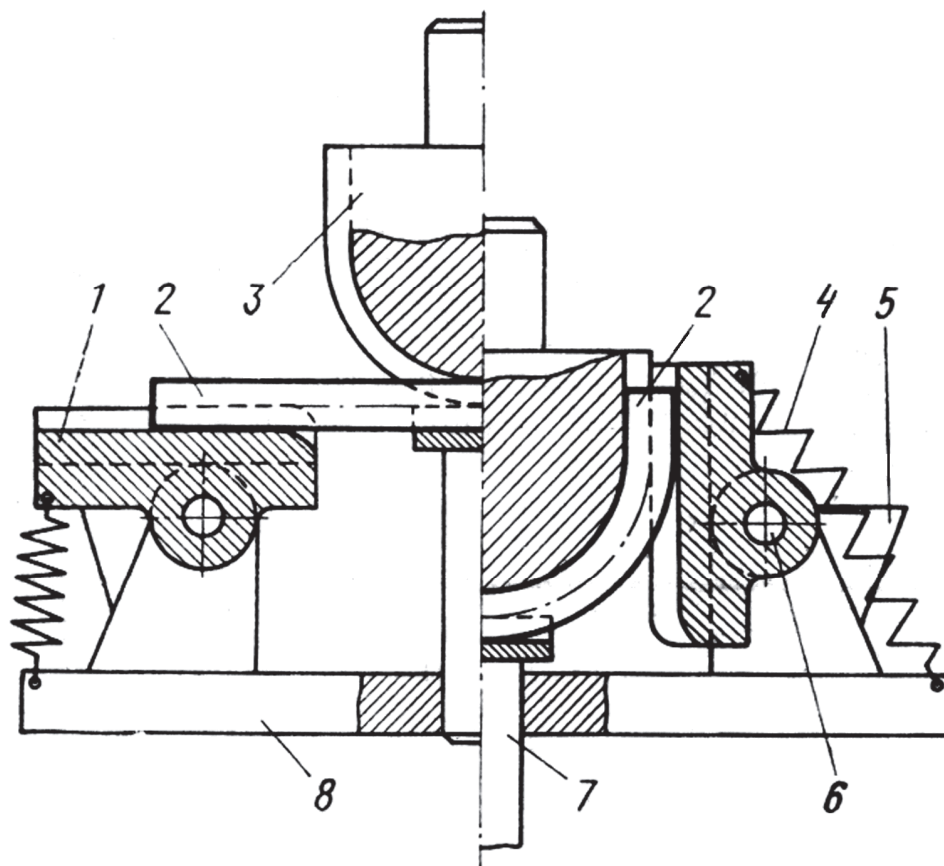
Трубогибочный штамп с поворотными сухарями:
